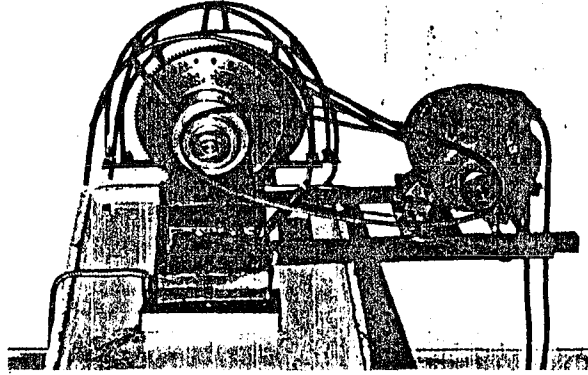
Polimer beton ve dökme demir tezgah gövdeleri
